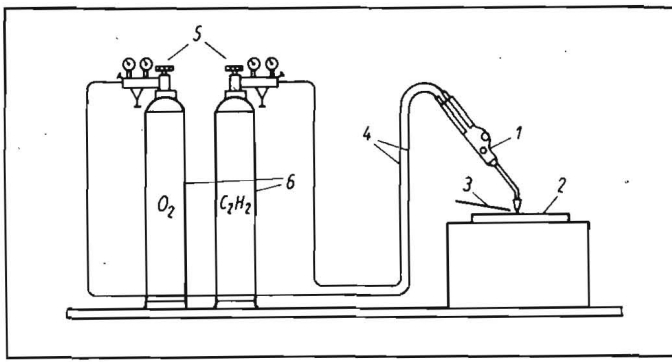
Aufbau eines Schweißplatzes zum Gas-Schweißen;
